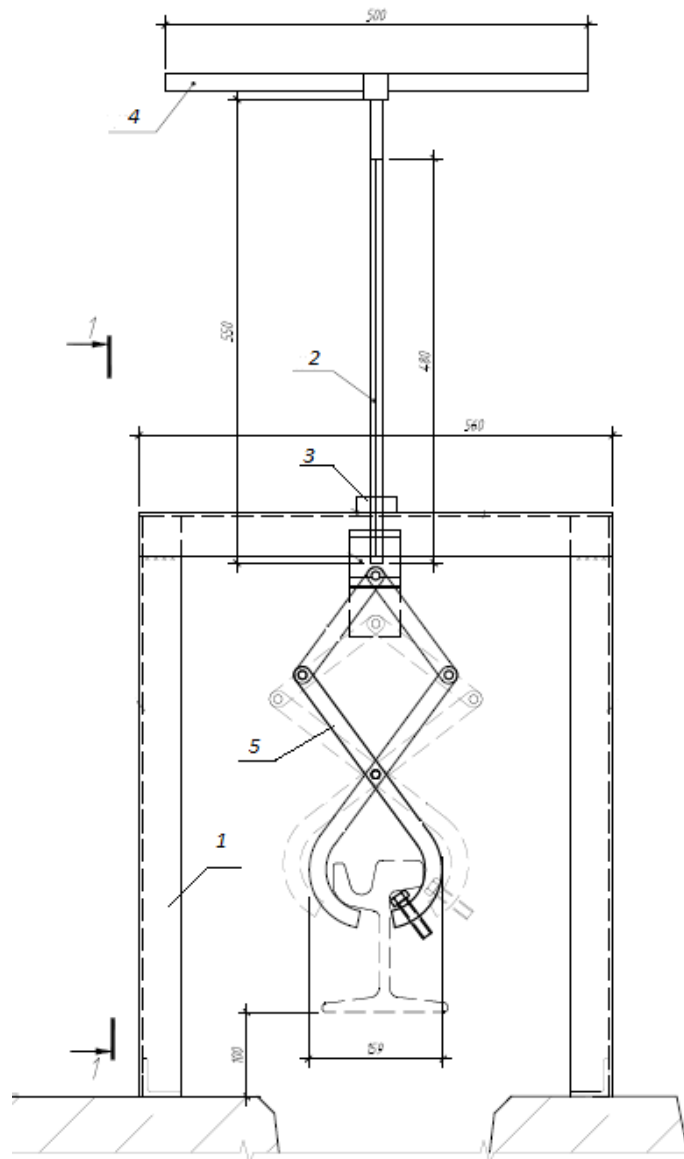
Кондуктор для установлення рейки в підрейковий канал
